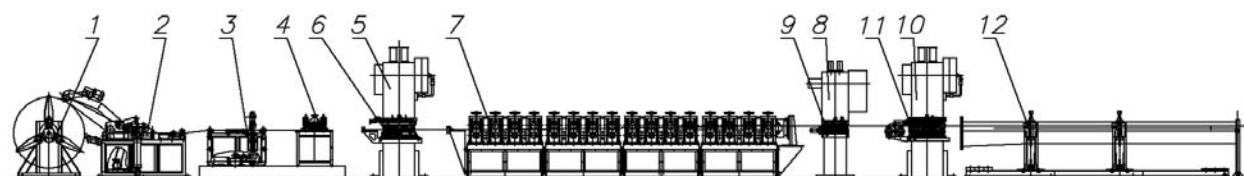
Линия изготовления детали «Балка» и «Стойка» для дорожного ограждения: 1 - разматыватель рулона, 2 - отгибатель края рулона, 3 - ножницы гильотинные, 4 - пост сварочный, 5 - пресс кривошипный, 6 - штамп перфорирующий, 7 - гибочно-прокатный станок, 8, 10 - пресс кривошипный, 9 - штамп перфорирующий, 11 - штамп отрезной, 12 - стол приемный
